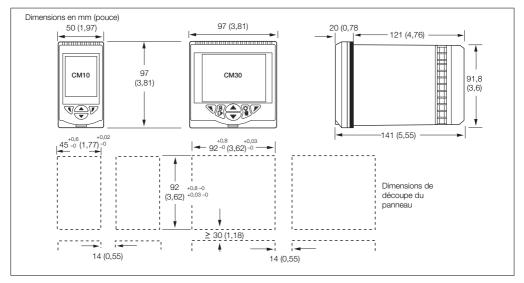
Dimensions des ControlMaster CM10 et CM30
